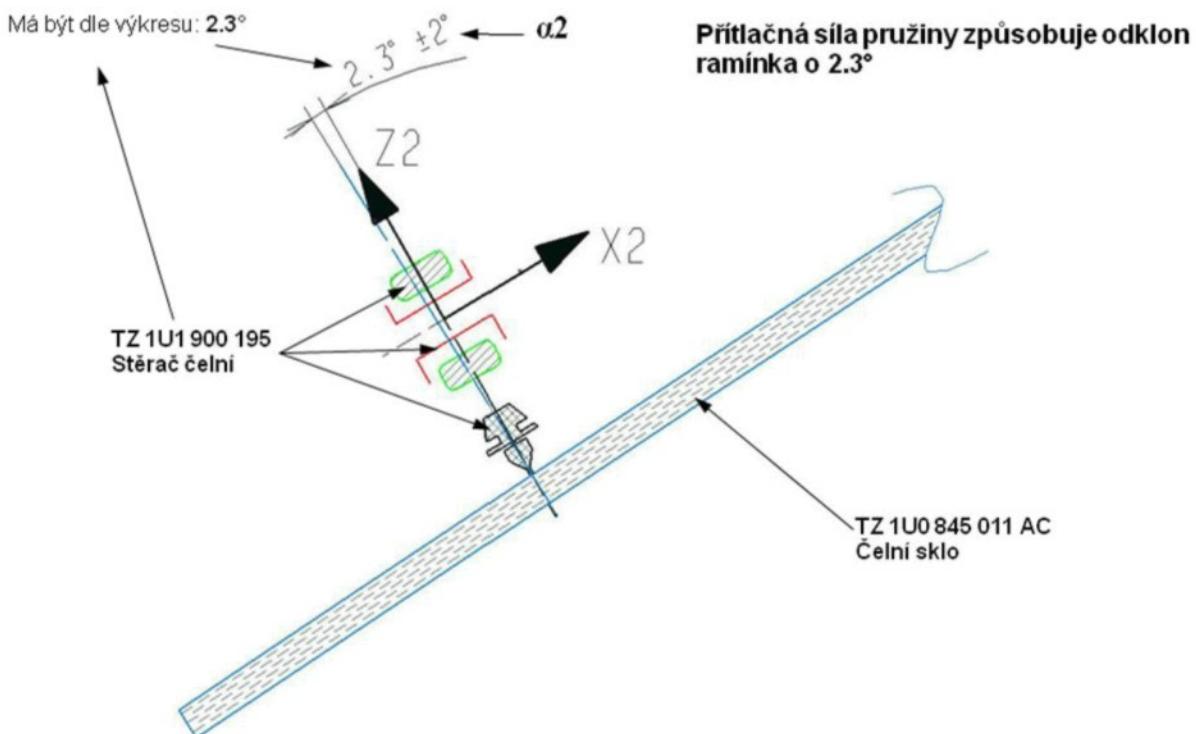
Natočení stěračové soupravy vlivem tolerance plechů – aritmetický součet tolerancí
